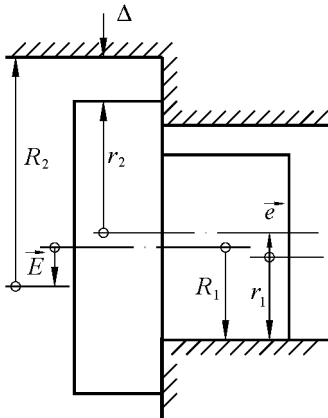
Расчетная схема сопряжения по гладкой и резьбовой поверхностям
